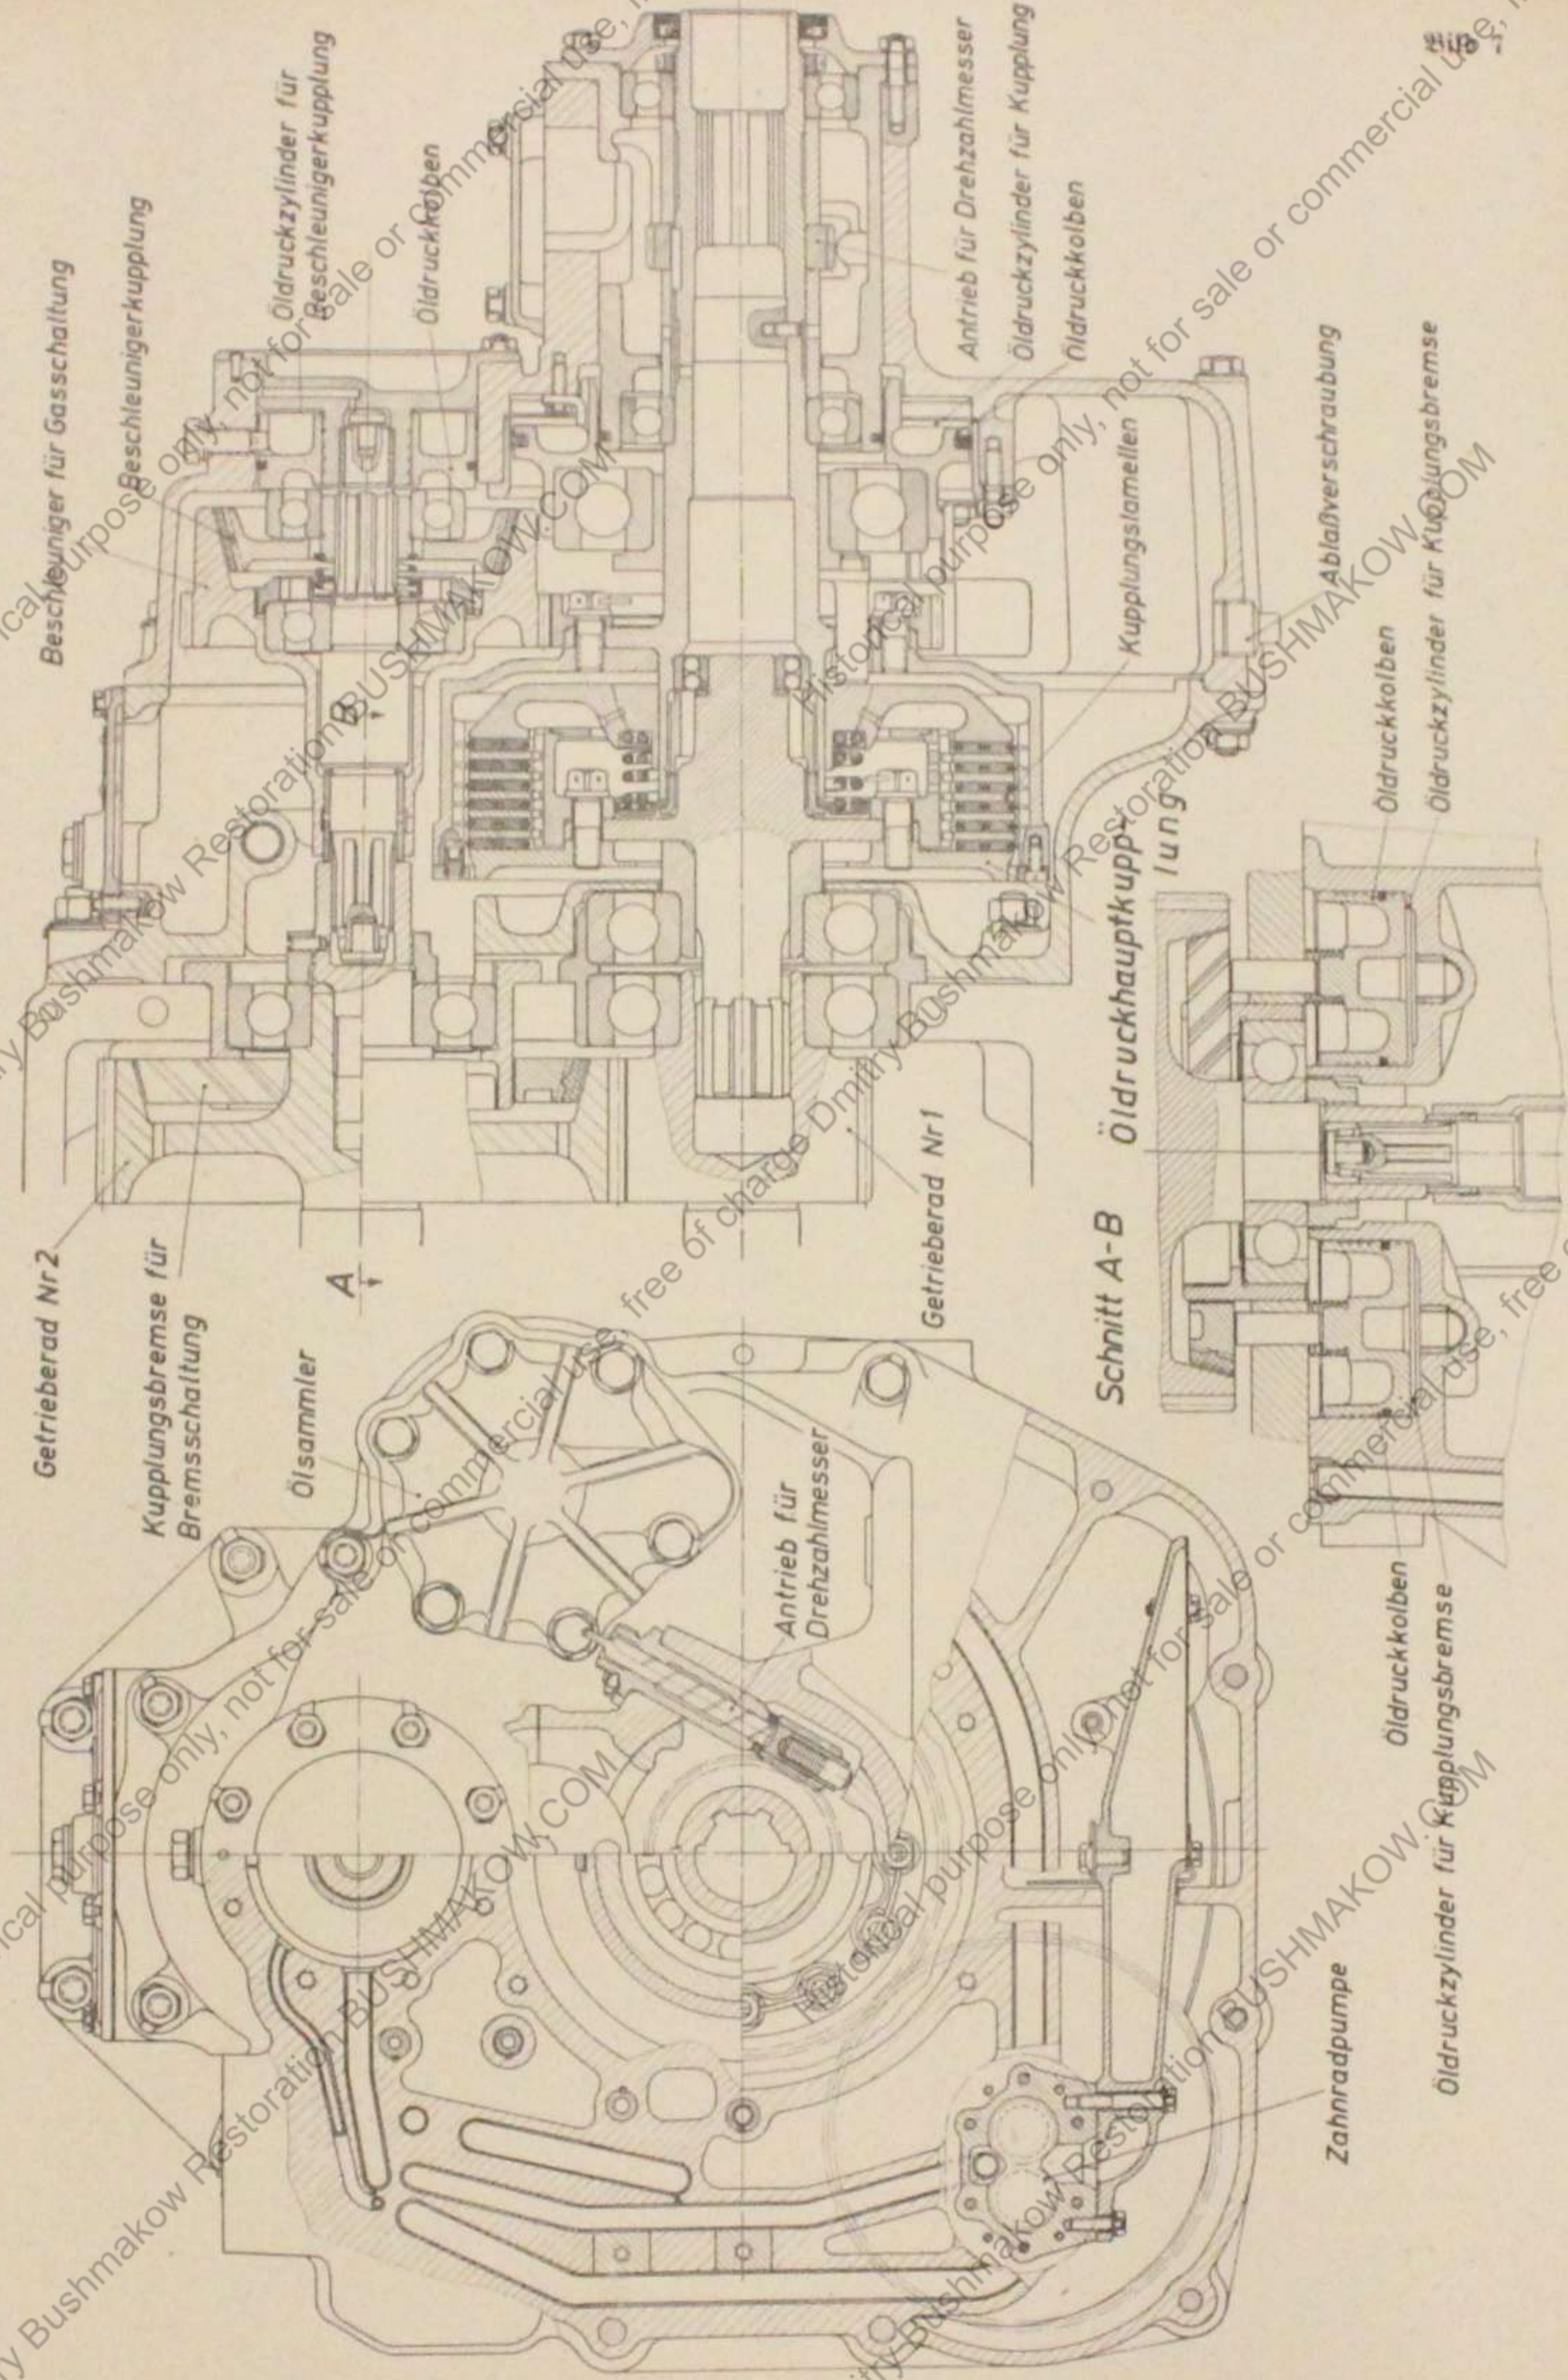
Hauptkupplung und Beschleuniger, Ausf. A
